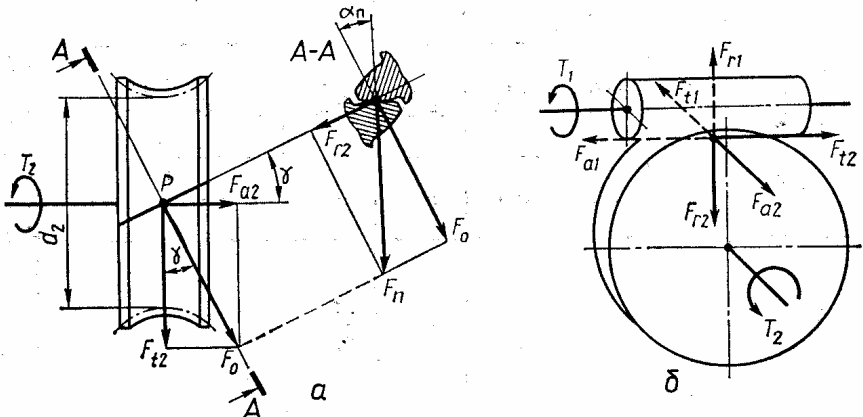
Зусилля на зубці черв'ячного колеса (а) і витки черв'яка (б)
